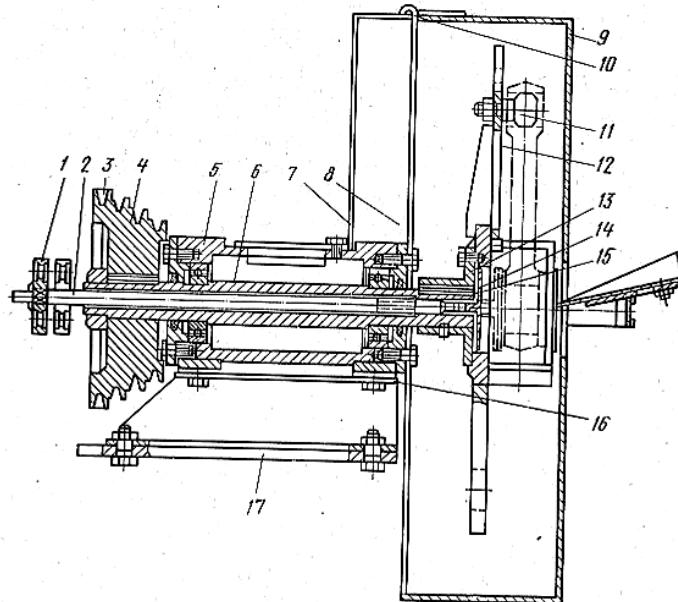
Приспособление для центробежной заливки шатунов:
